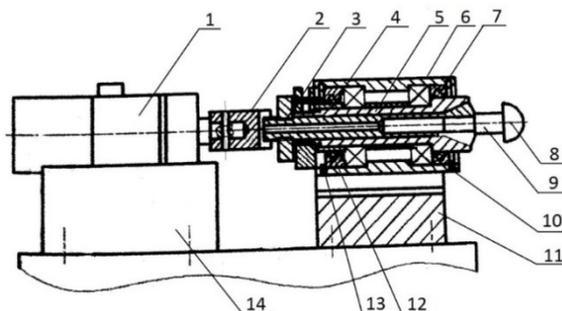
Шпиндель станка для обработки сферических кабошонов
